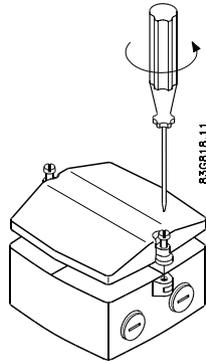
Abdeckung des Anschlusskastens entfernen
